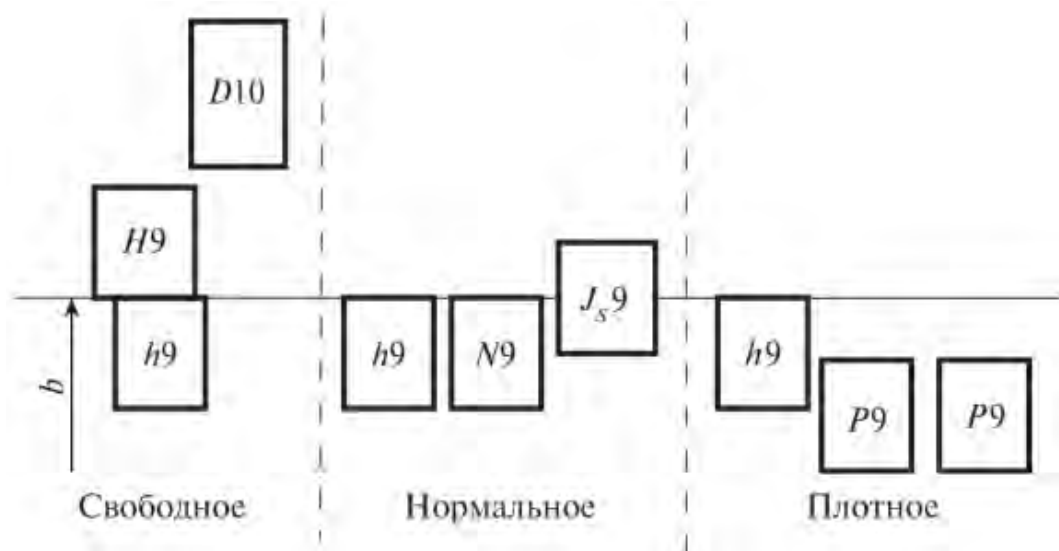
Схема полей допусков шпоночного соединения с призматической шпонкой
